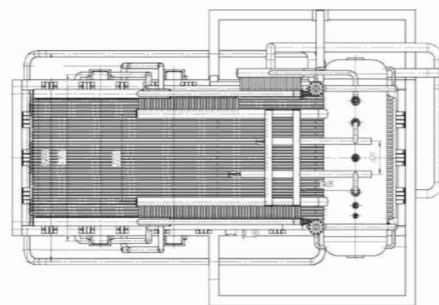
Общий вид котла Е-30-3,9-440ДФ
